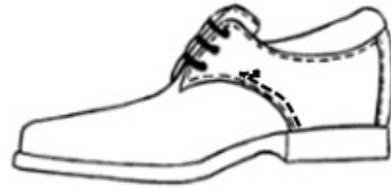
Схема сборки заготовки верха полуботинка с настрочными берцами
